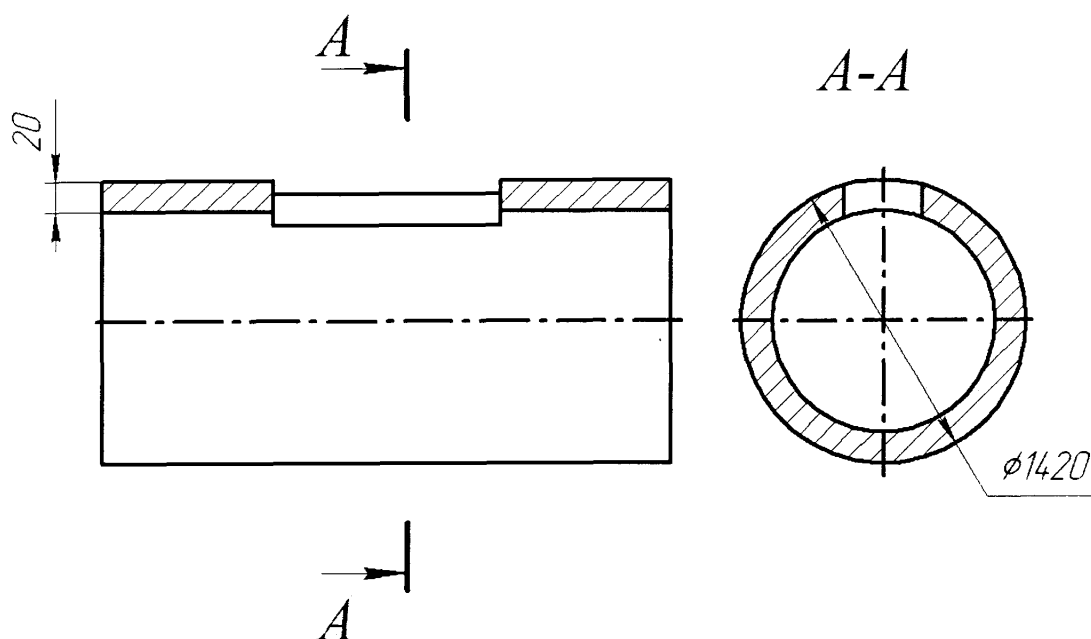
Ескіз місця вирізання заготовки для зразка
